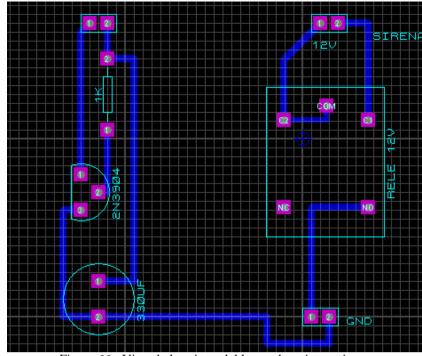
Vista de las pistas del lector de tarjeta y sirena Fuente: Autores
